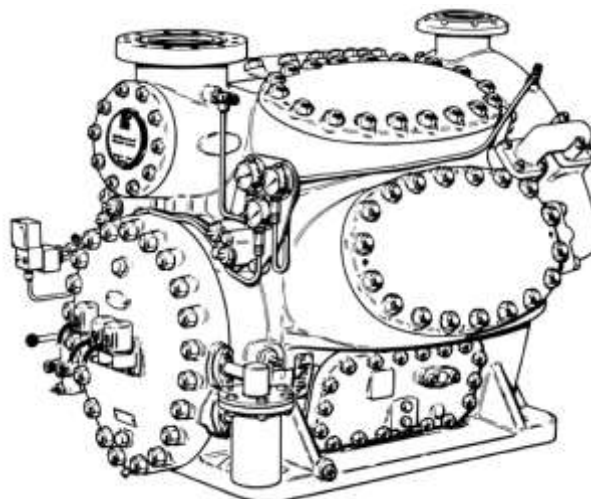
Assemblaggio di un compressore alternativo a 4 cilindri
